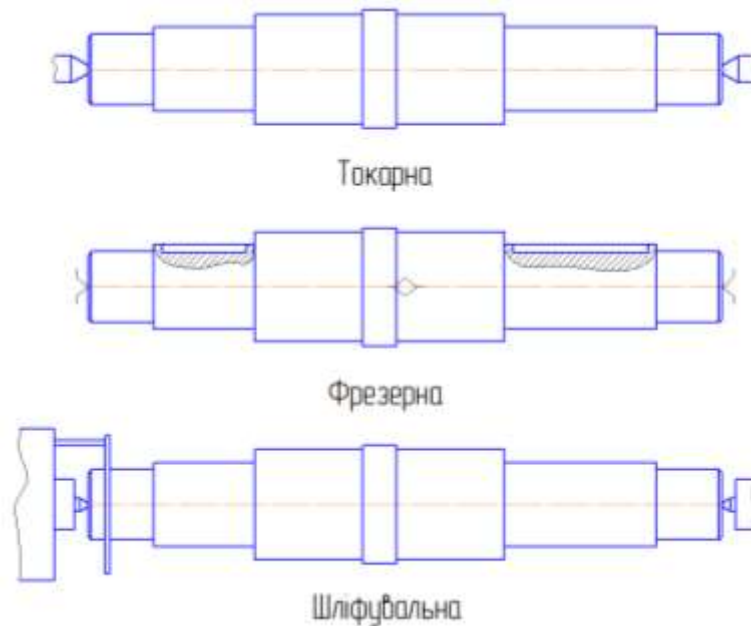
Схеми базування заготовки під час механічної обробки вала
